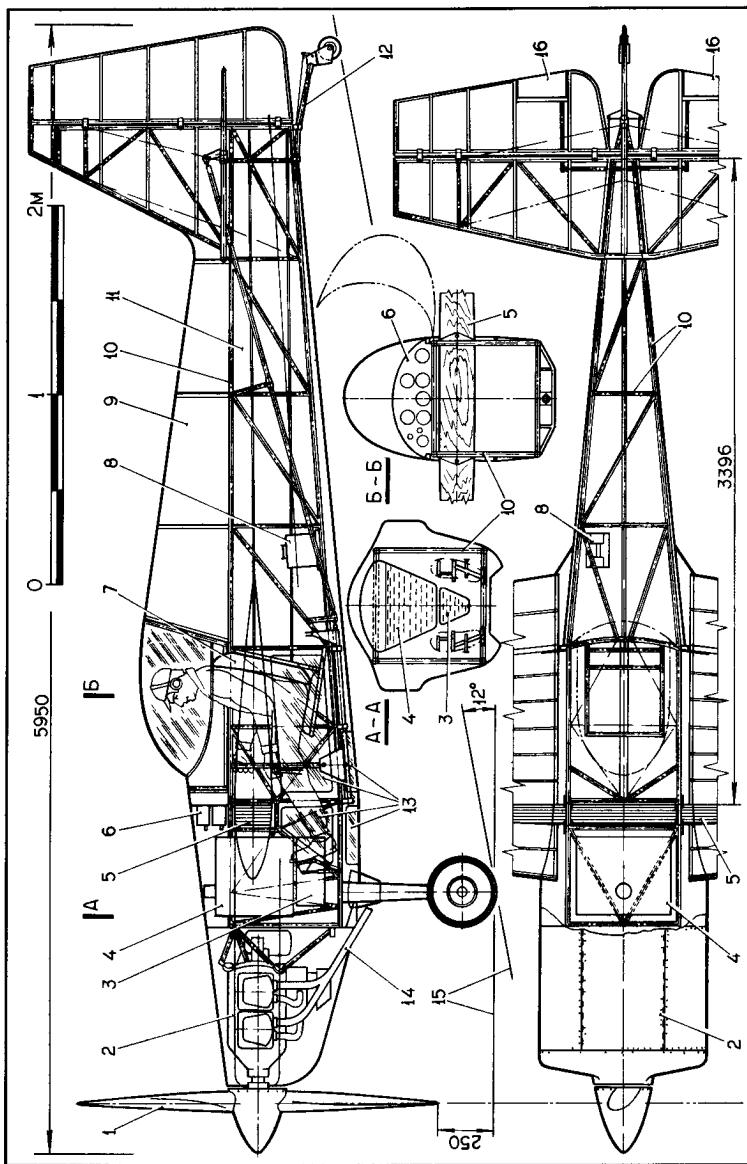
Компоновка спортивно-пилотажного самолета «Ласта»:
